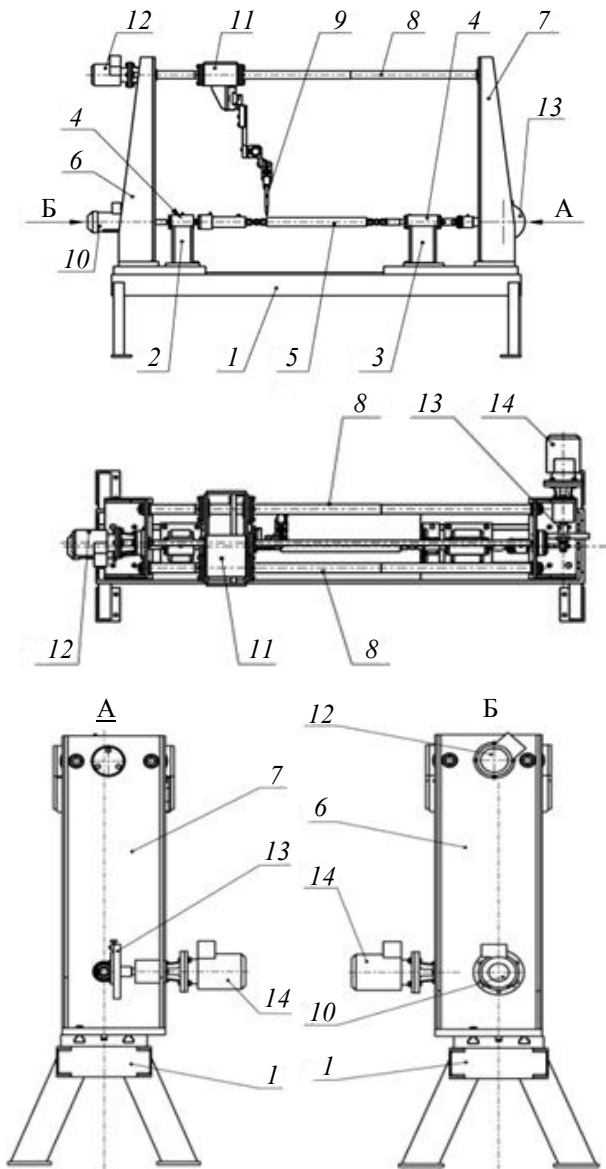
Установка автоматической дуговой наплавки тел вращения с управляемыми импульсными механическими колебаниями изделия:
